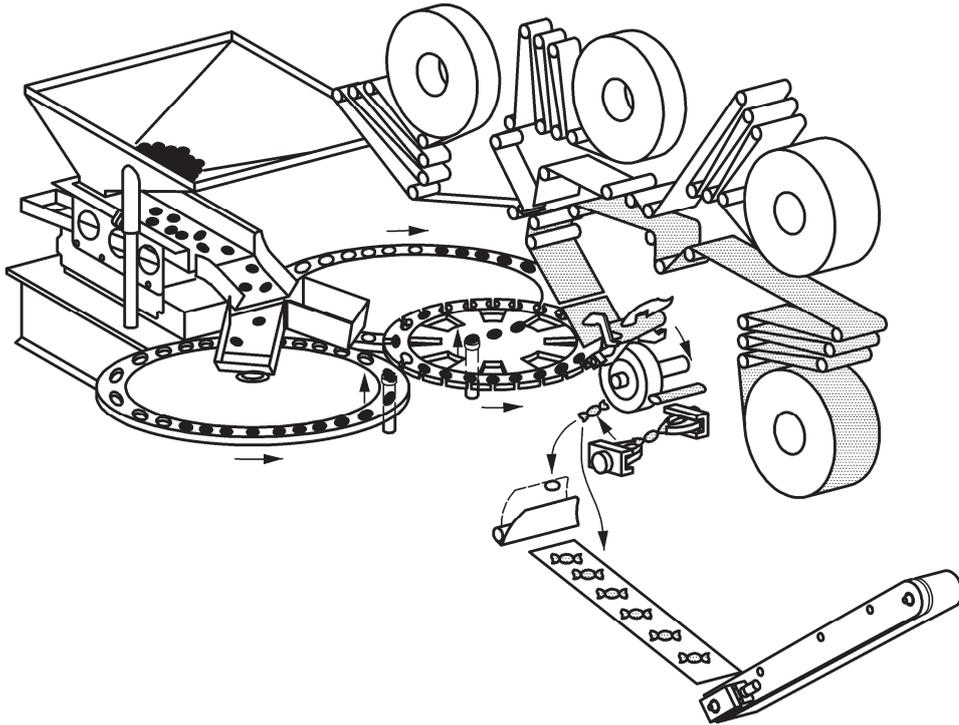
Einschlagmaschine für ein extrudiertes Produkt
